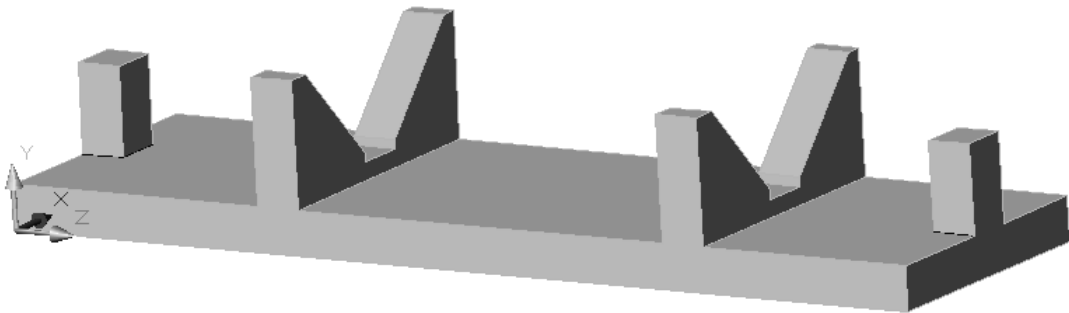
Кассета для размещения заготовки на шаговом конвейере
